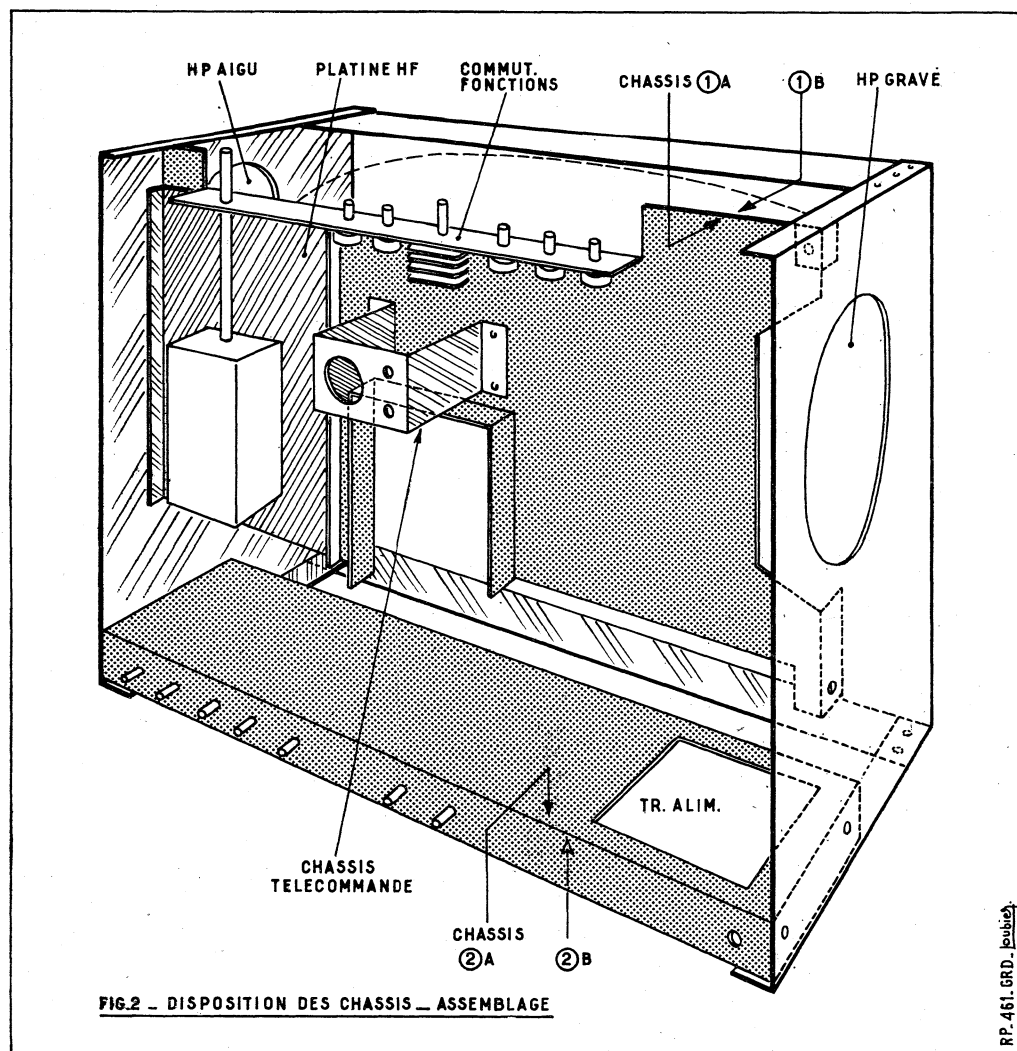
DISPOSITION DES CHASSIS - ASSEMBLAGE
